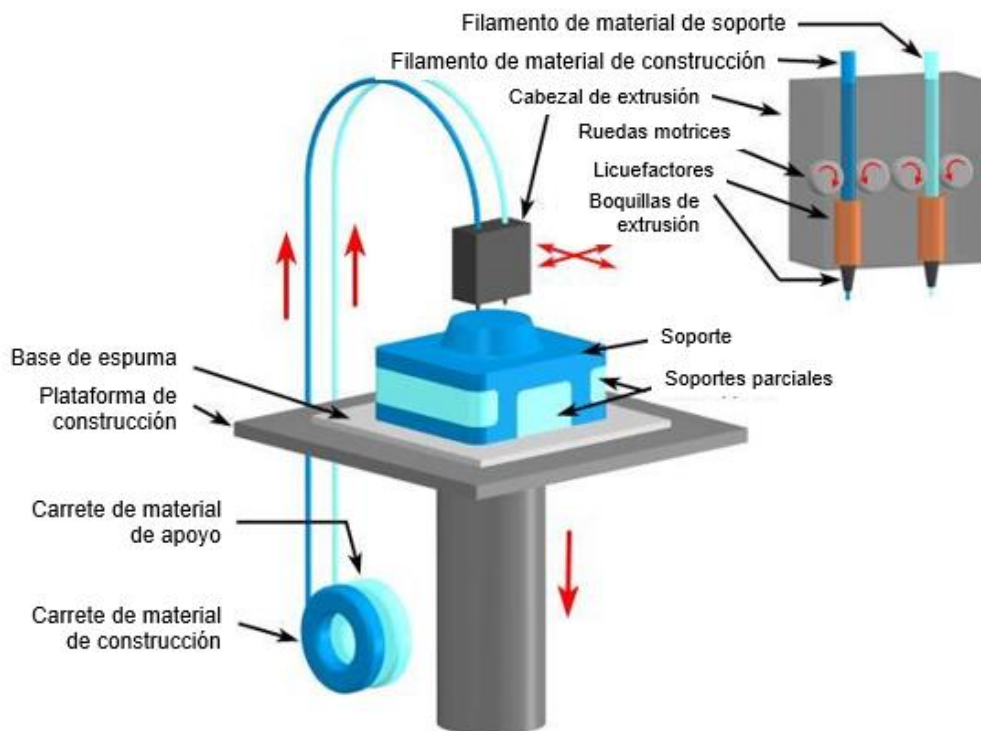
Impresión 3D por extrusión (GeneratePress, 2022)
